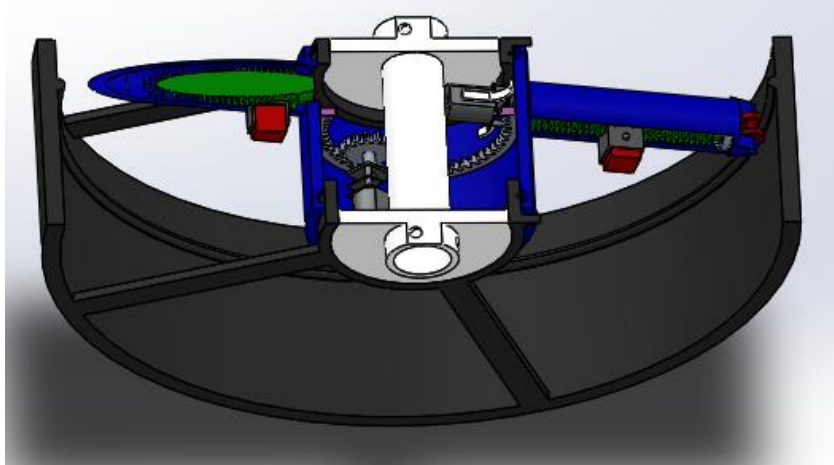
Disco de Balanceo Activo Ensamblado.
